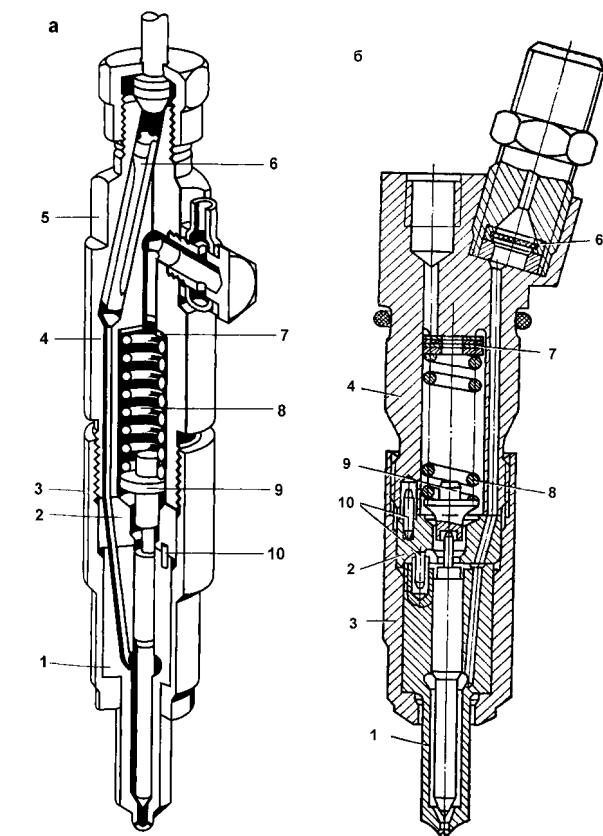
Автомобильные форсунки с укороченной штангой: а - стандартная фирмы R.Bosch; б - ЯЗДА (для КамАЗ): 1 - распылитель; 2 - проставка; 3 - стяжная гайка; 4 - корпус; 5 - крепежные выфрезеровки; 6 - фильтр; 7 - регулировочные прокладки; 8 - запорная пружина; 9 - тарелка; 10 - штифт.
